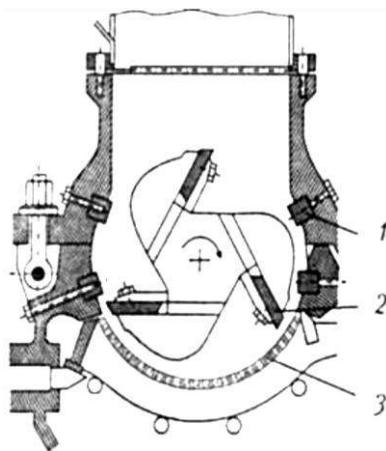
Ножевая дробилка: 1 – неподвижный нож; 2 – подвижный нож; 3 – сито [15]
